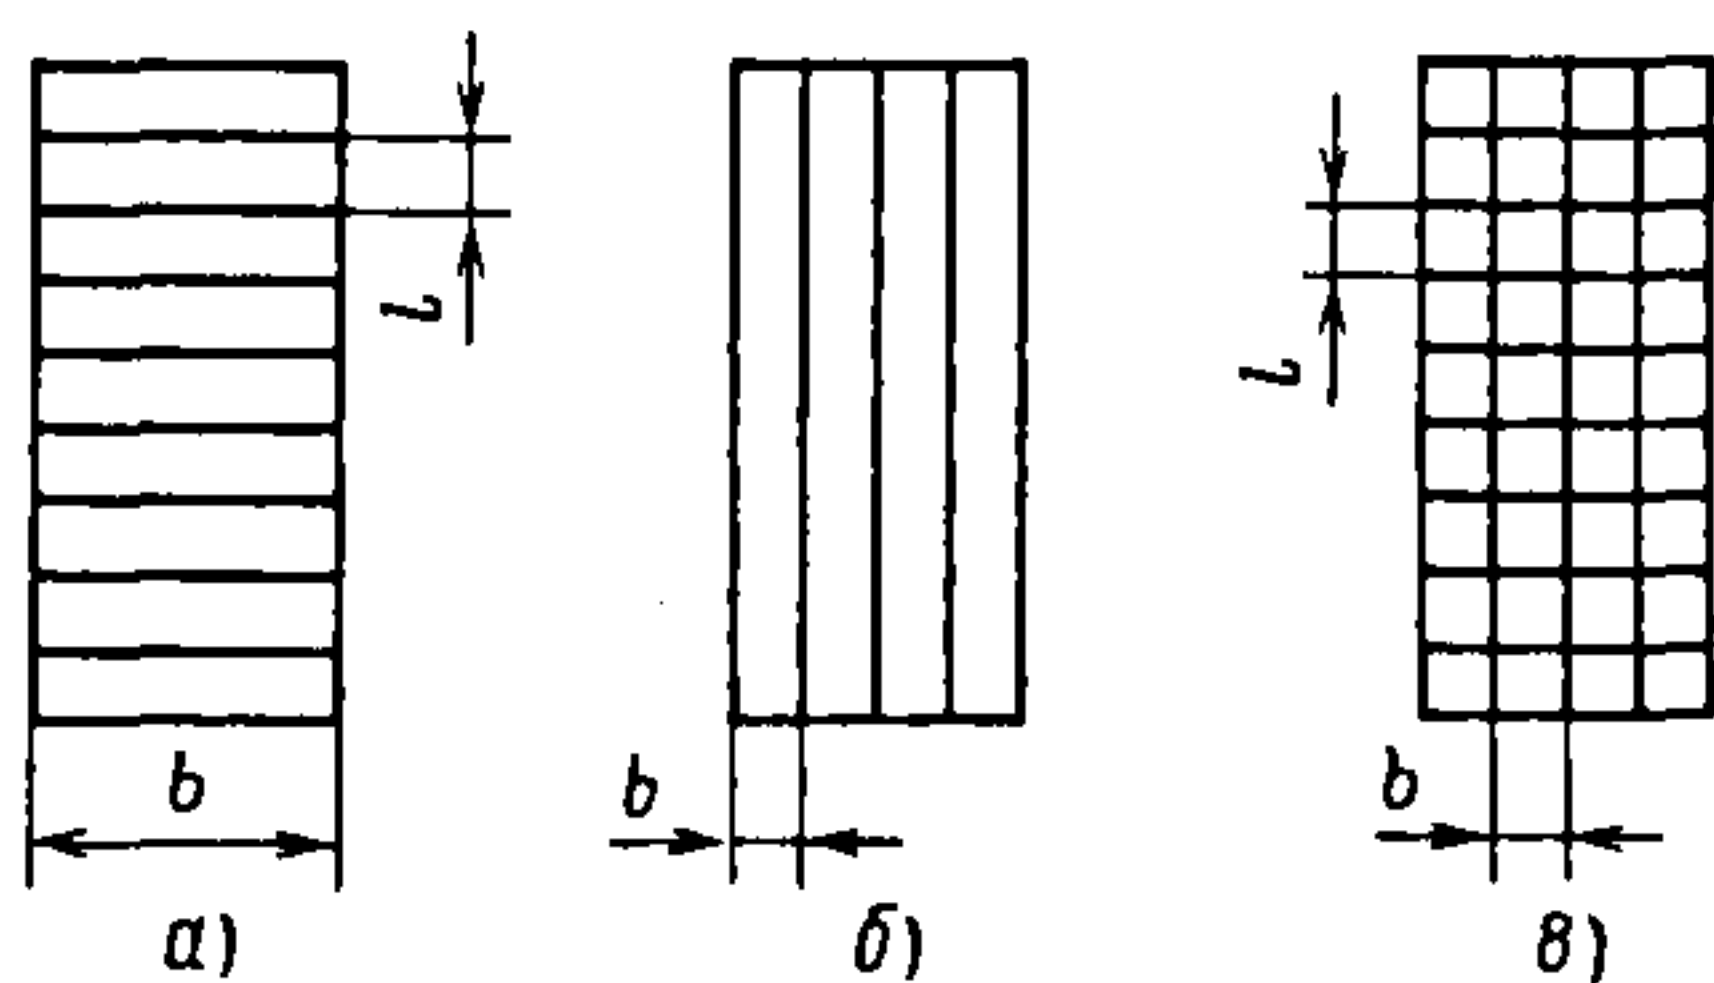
Схемы укрепления ребрами плоских прямоугольных стенок:
